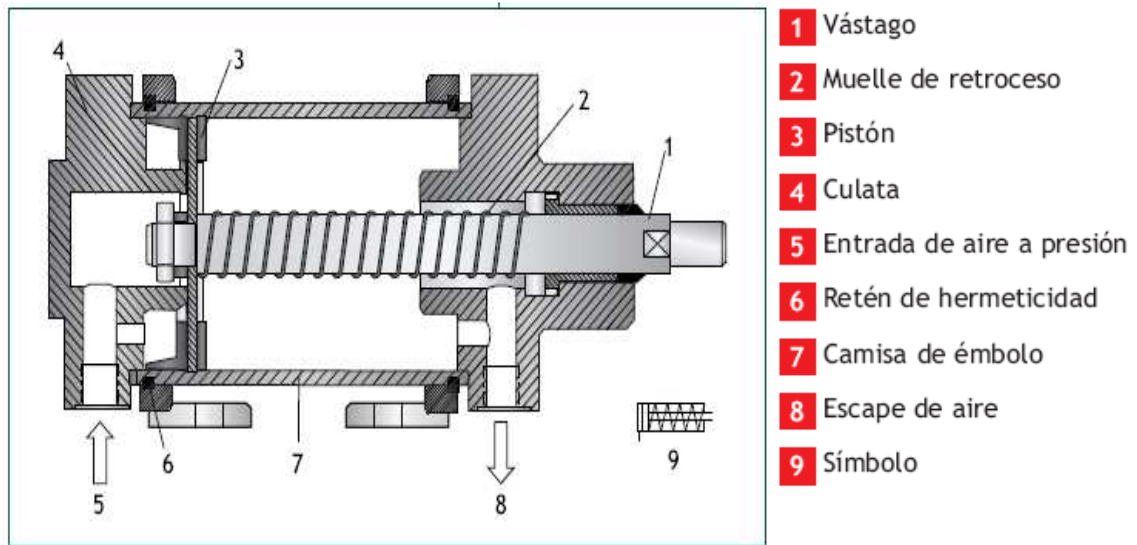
Cilindro de émbolo de simple efecto seccionado.
